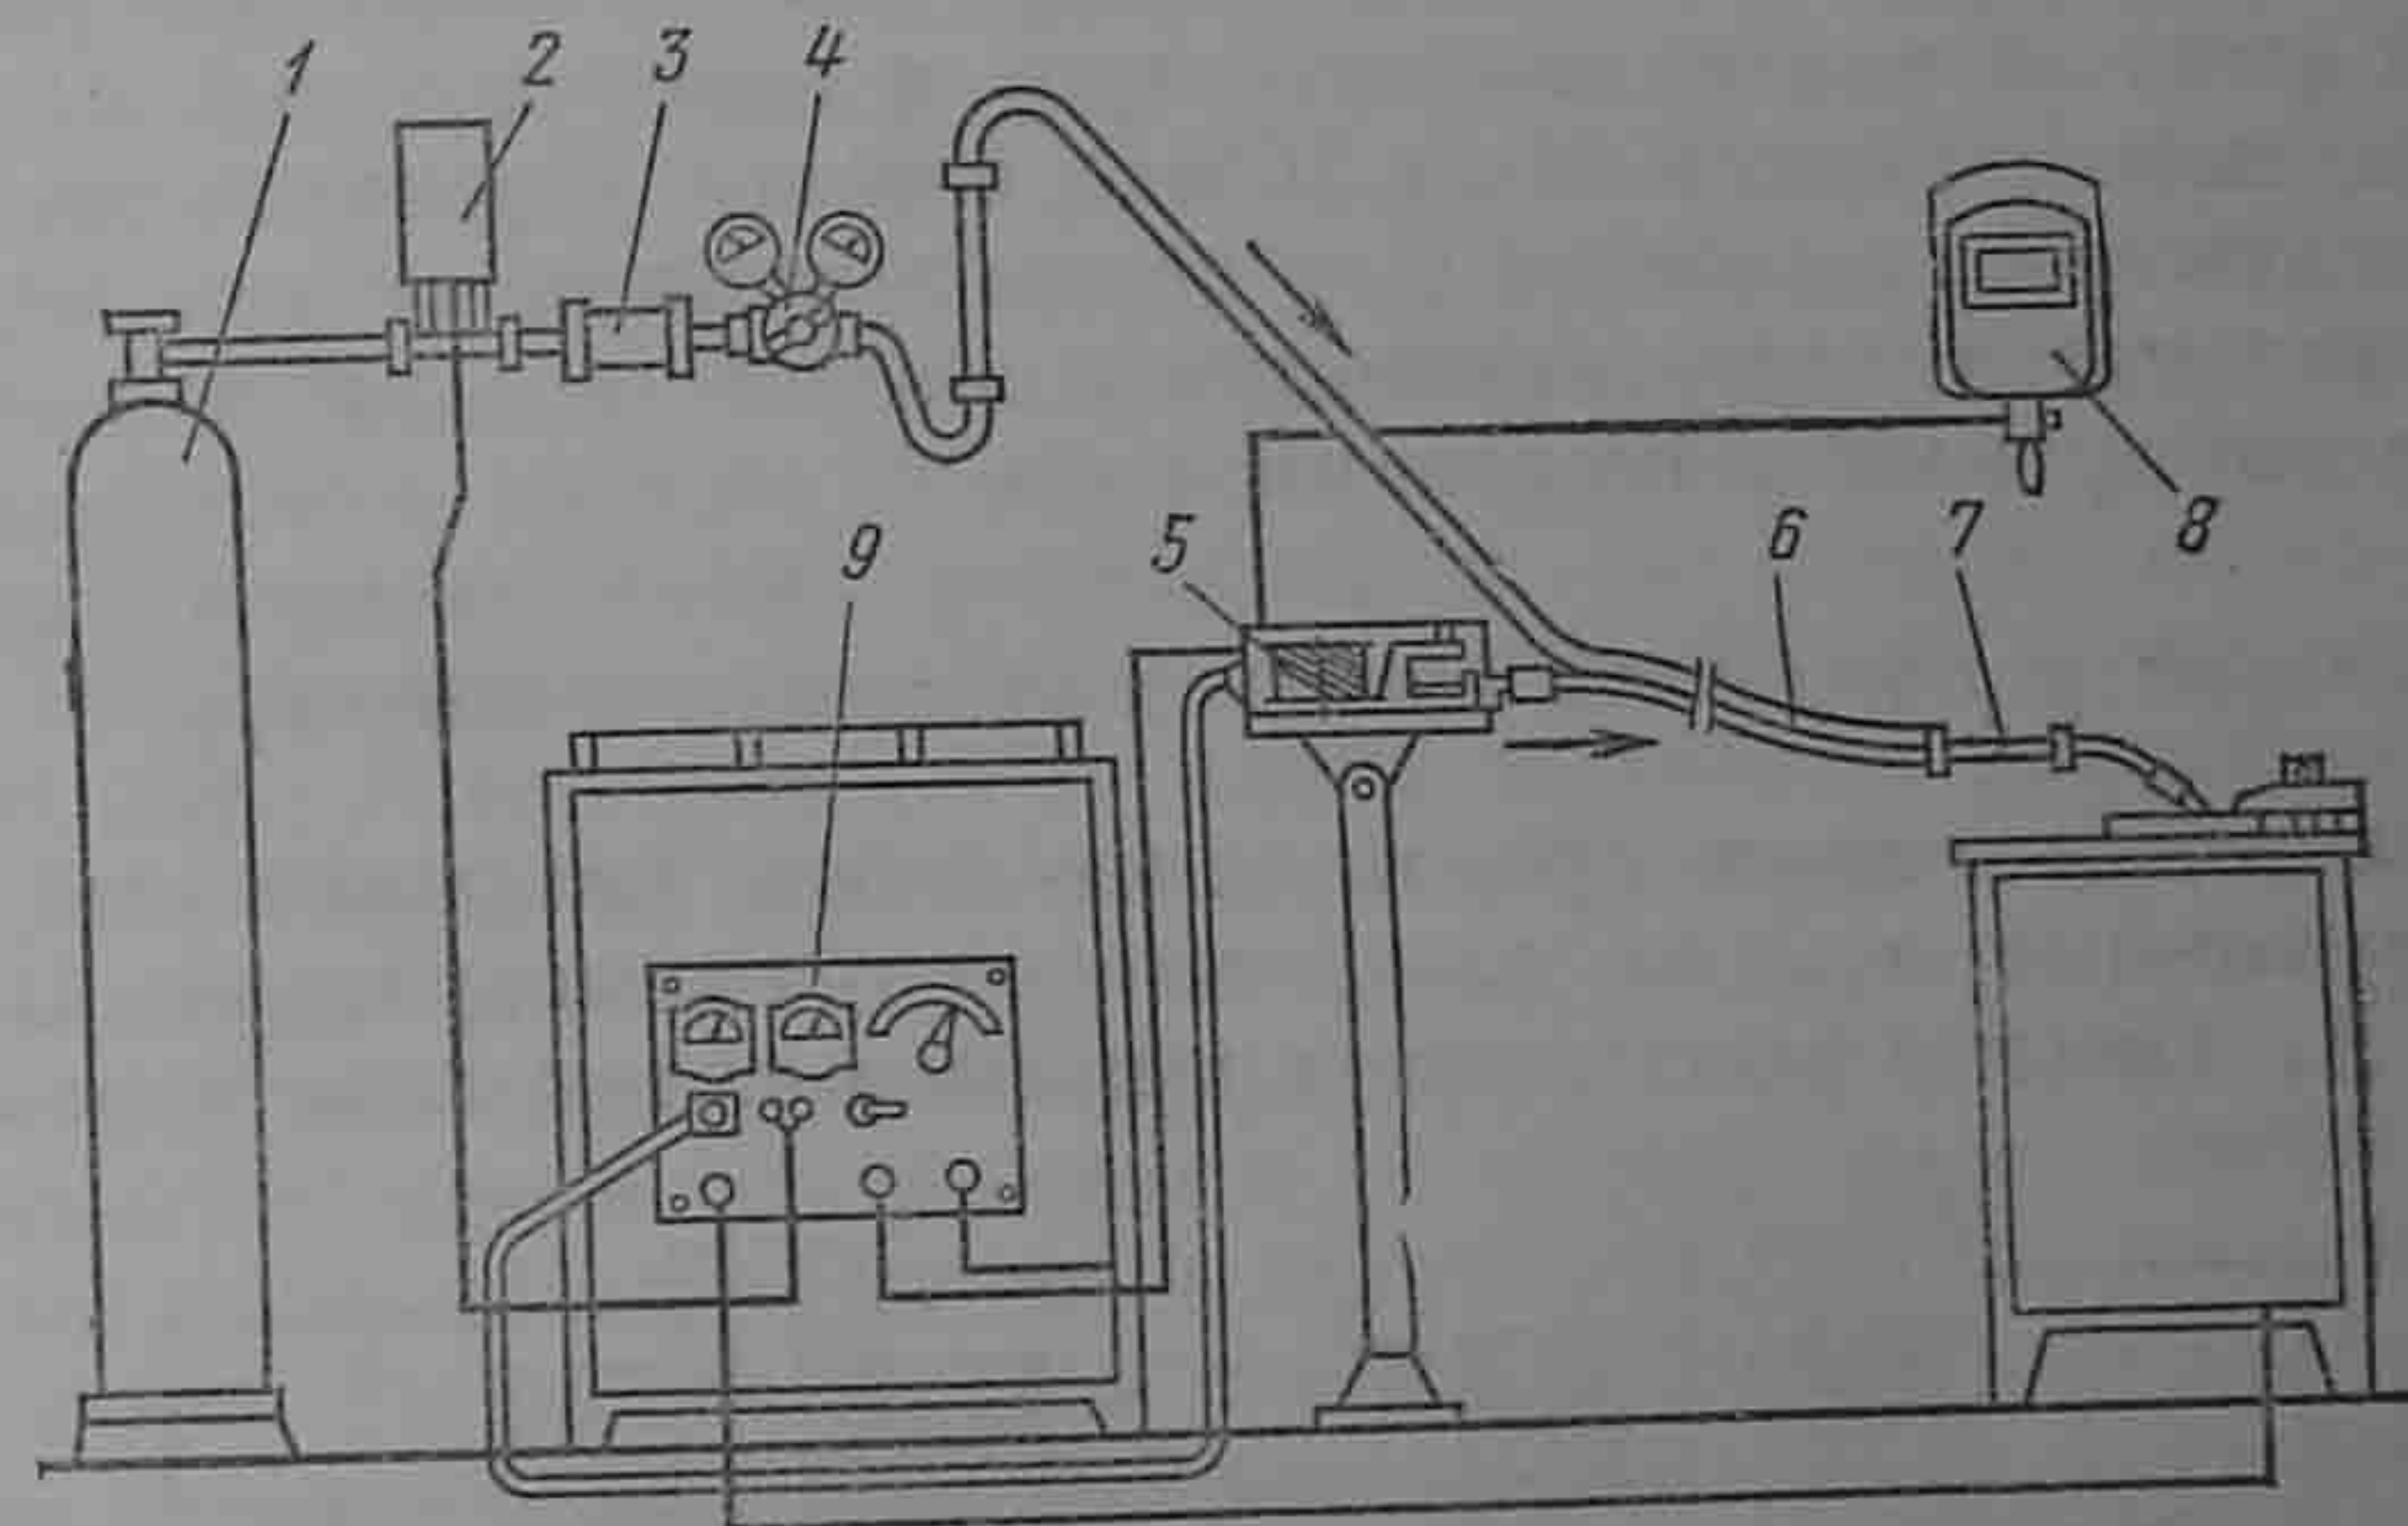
Оборудование поста для сварки в защитных газах
